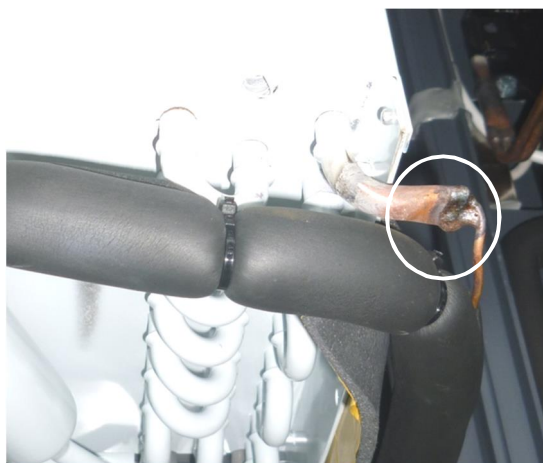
Operação de soldadura evaporador - capilar
